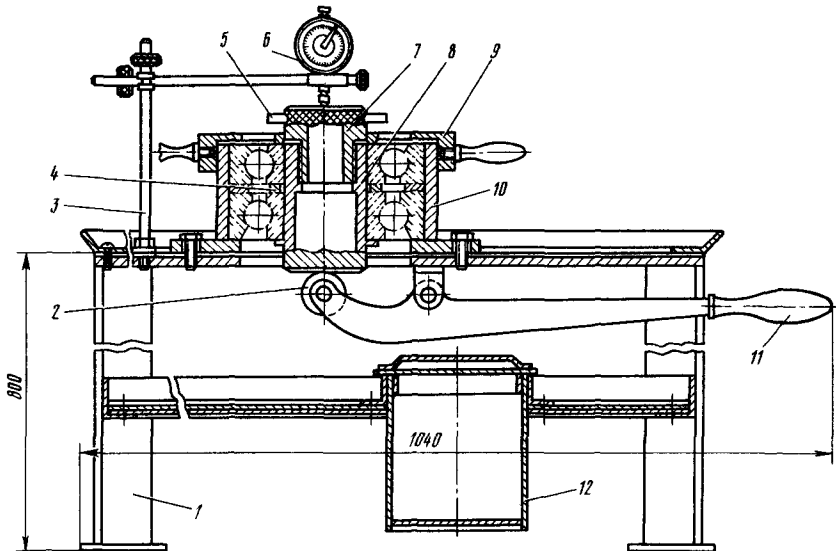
Стенд для регулирования натяга комплекта опорно-упорного подшипника воздуходувки дизеля 2Д100:
